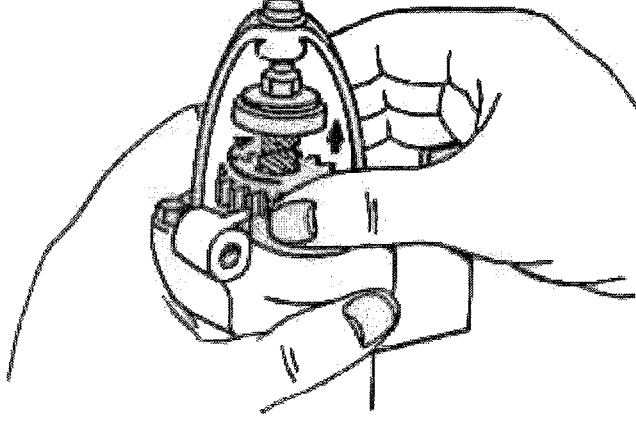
Mekanik ilk hareket (Miller & Miller, 1993)
